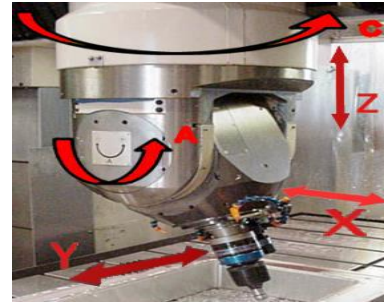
Компоновка осей пятиосевых фрезерных станков с поворотной шпиндельной головкой
